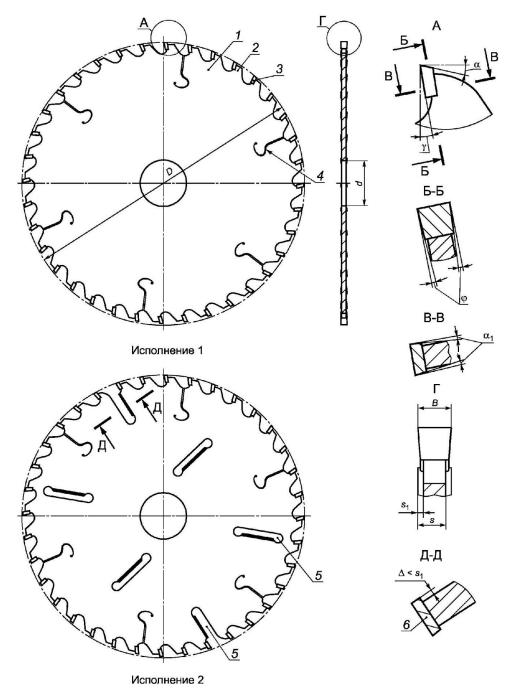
Дисковые пилы тип 1 для бревнопильных станков: 1 - корпус; 2 - зуб; 3 - твердосплавная пластина; 4 - компенсаторы; 5 и 6 - окна и пластины очистителей пропила
